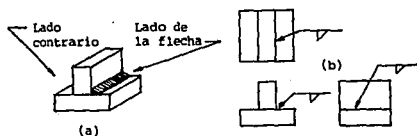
Representación ortogonal de una soldadura de filete.
